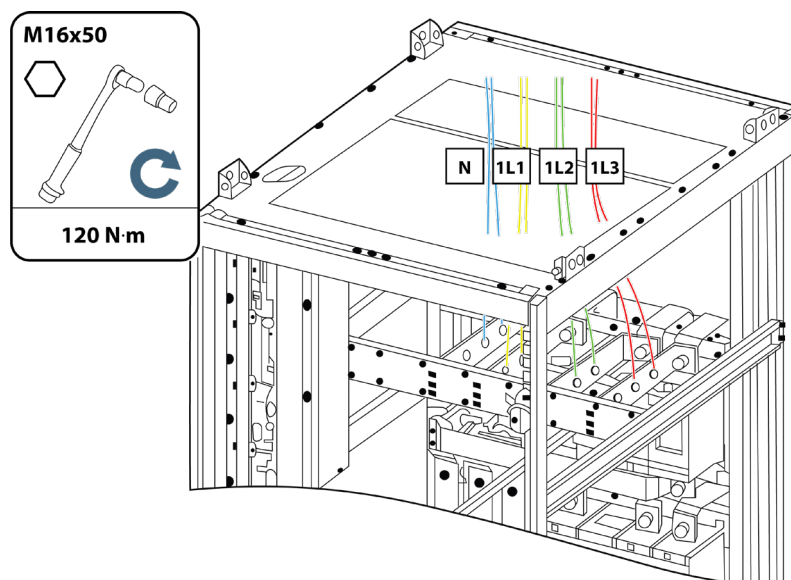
CONEXIÓN DE CABLEADO DE ALIMENTACIÓN.
